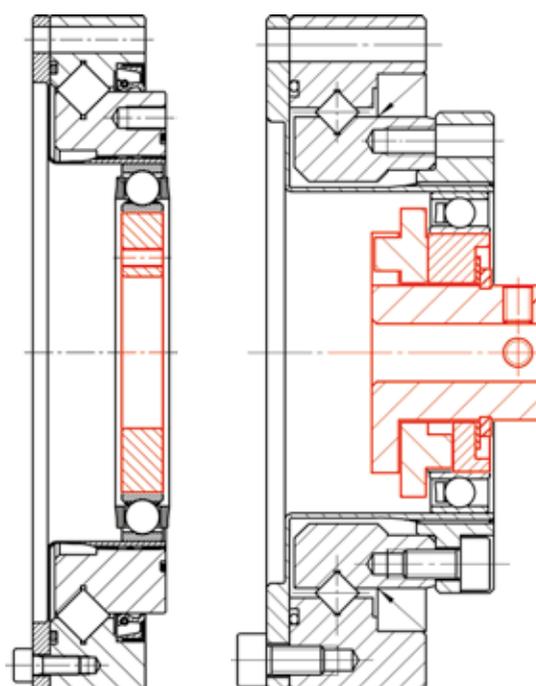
Конструкция волнового редуктора с полым валом (выделен цветом)
